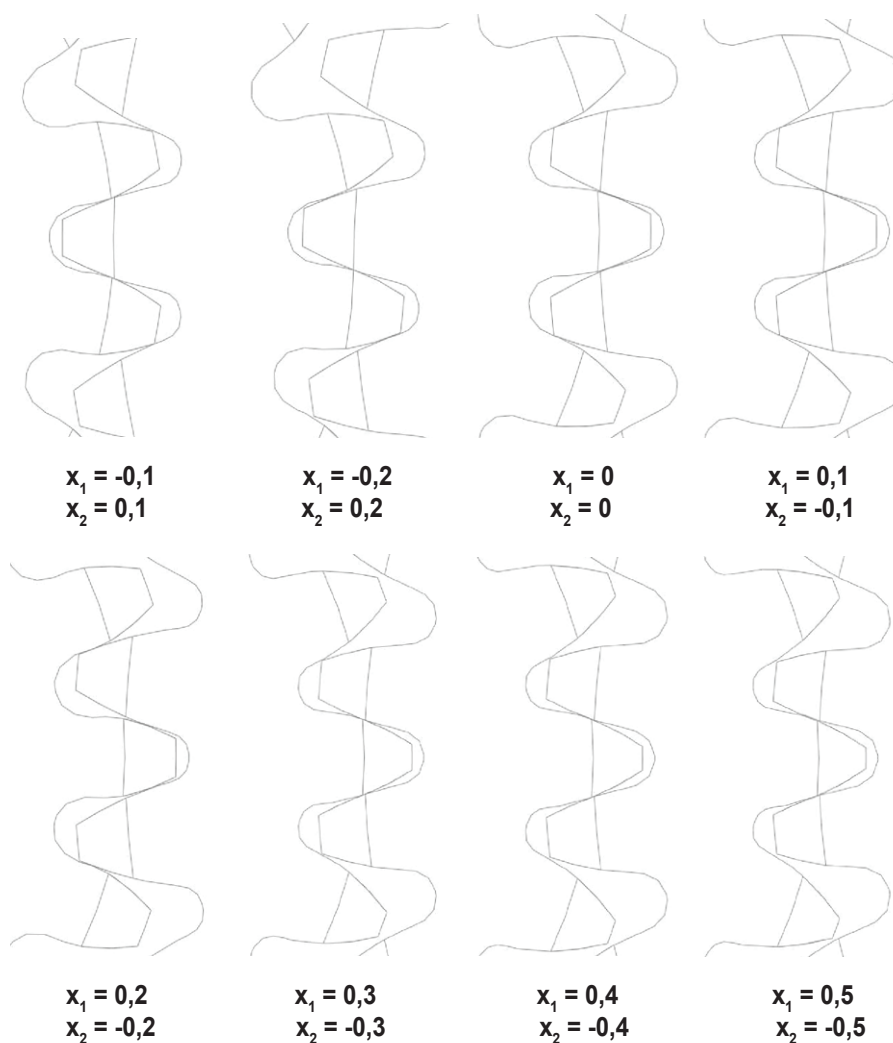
Геометрія зовнішнього зачеплення циліндричної зубчастої передачі (шестерня ліворуч, зубчасте колесо праворуч)
